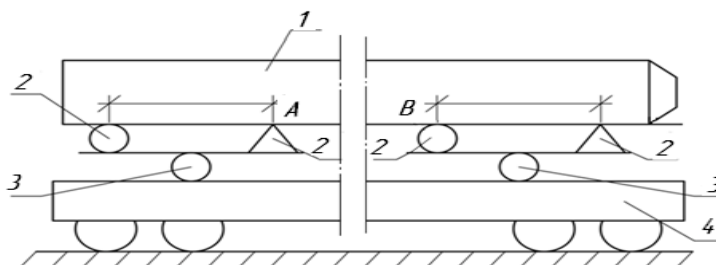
Вариант размещения корпуса ракеты на 4-х ложементах, где 1 – корпус ракеты; 2, 3 – опоры; 4 - платформа
